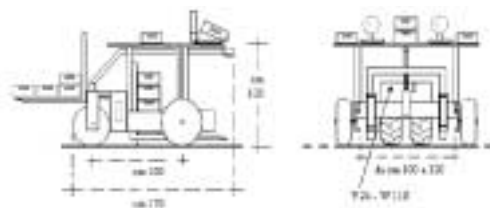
Progetto dell'agevolatrice a 2 posti: vista laterale (sx) e posteriore (dx).
